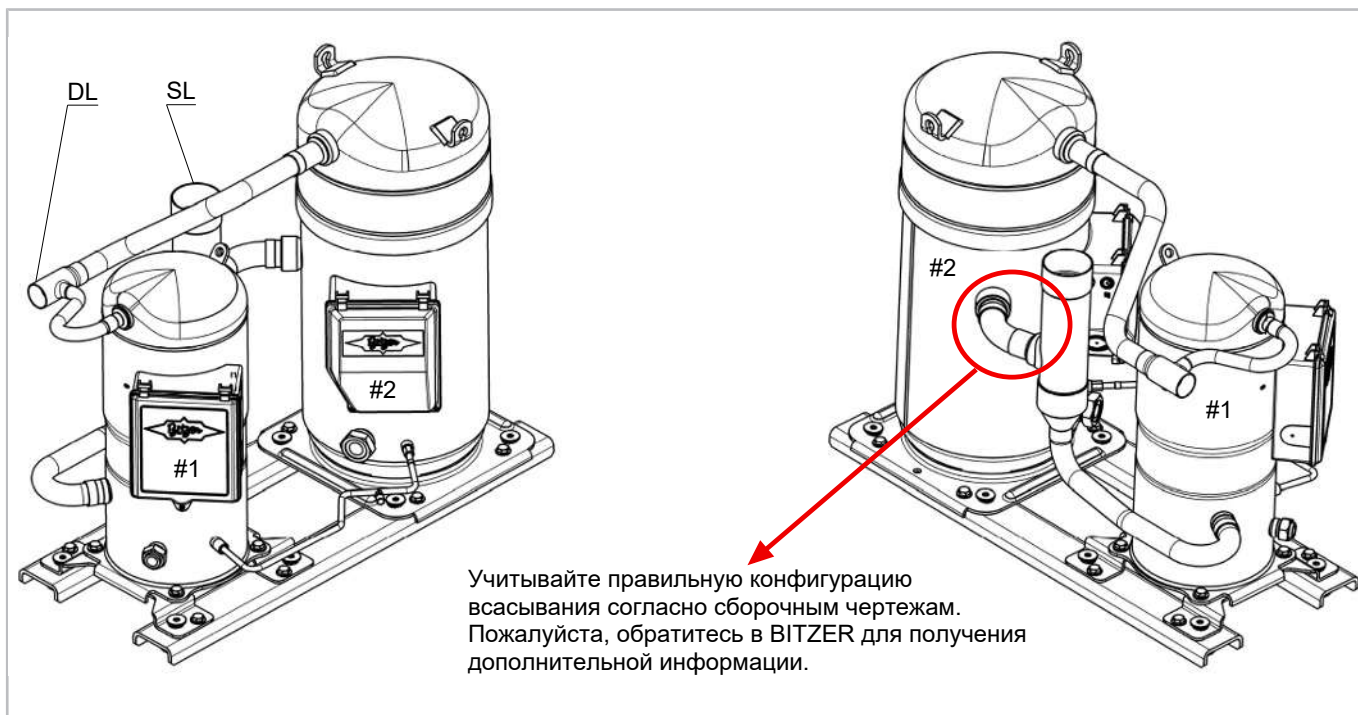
Пример смешанного тандем объединения ORBIT 6 и компрессоров ORBIT 8 с BITZER Advanced Header Technology (вертикальный ВАНТ header)
